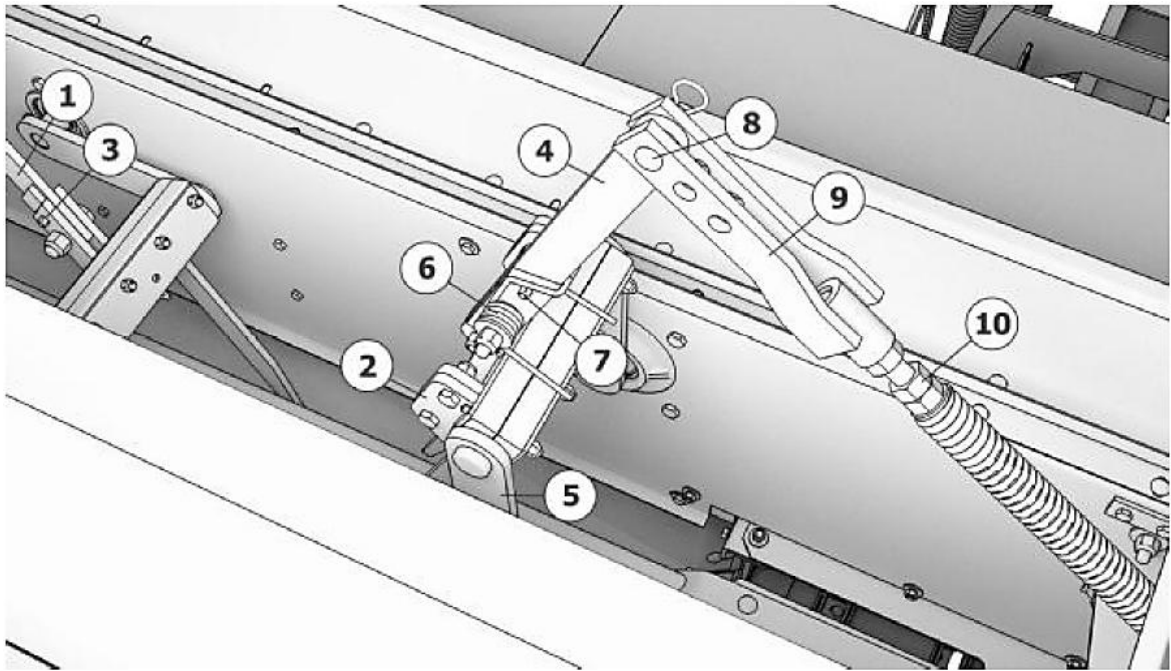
Подающие граблины: 1– двухпальцевая граблина; 2 – трехпальцевая граблина; 3 – срезной предохранительный болт; 4 – рычаг граблины; 5 – кривошип граблины; 6 – пружина кручения; 7 – срезной предохранительный болт; 8 – регулировочное отверстие; 9 – регулировочная тяга; 10 – гайка
